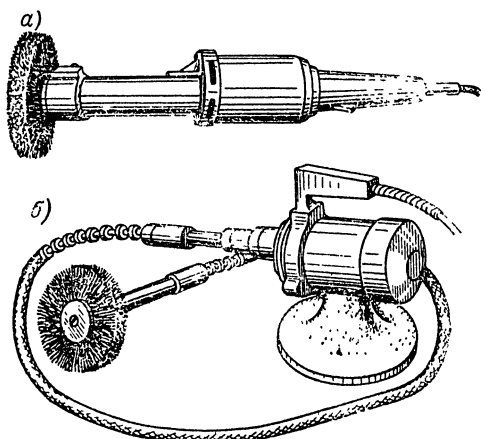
Универсальный механизированный инструмент для полирования: а — пневматический; б — электрический
